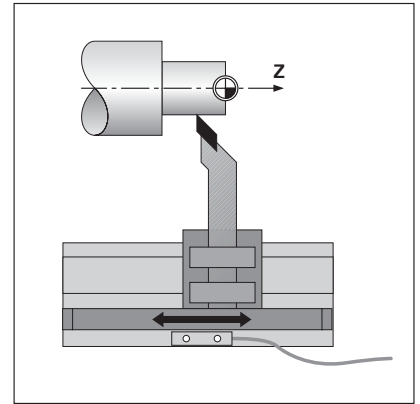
Wegmeßsystem für eine Linearachse, z.B. für die Z-Achse
